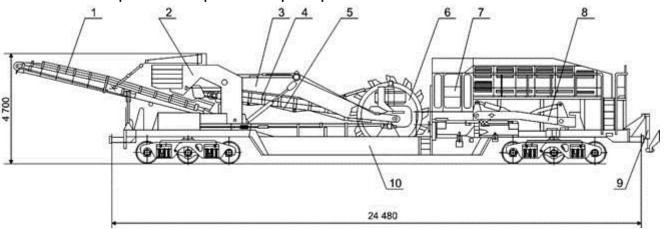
Расположение оборудования машины СЗП-600Р: 1 — поворотный конвейер; 2 — поворотный механизм; 3 — стрела ротора; 4 — основной конвейер; 5 — защитный конвейер; 6 — ротор; 7 — кабина управления; 8 — плуг; 9 — стабилизирующая опора; 10 — главная рама
